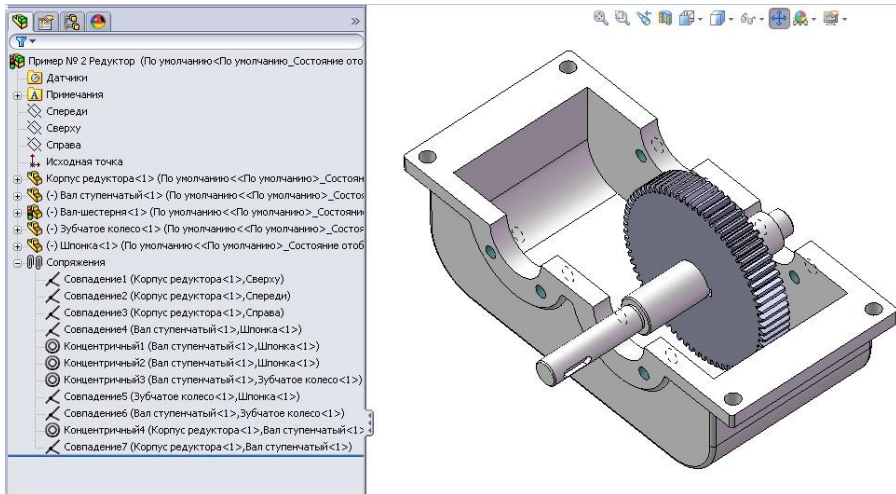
Вал зі шпонкою й зубчастим колесом у корпусі редуктора
